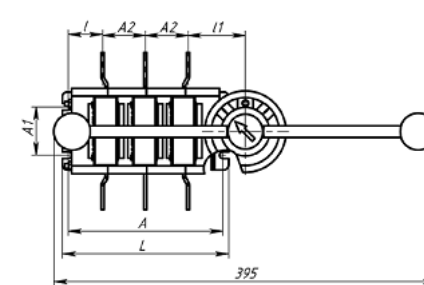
Б Выключатель-разъединитель на два направления 3-полюсный с передней поворотной рукояткой
